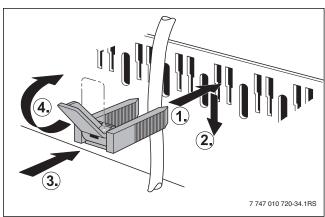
Fissaggio dei cavi mediante fascette serracavo
